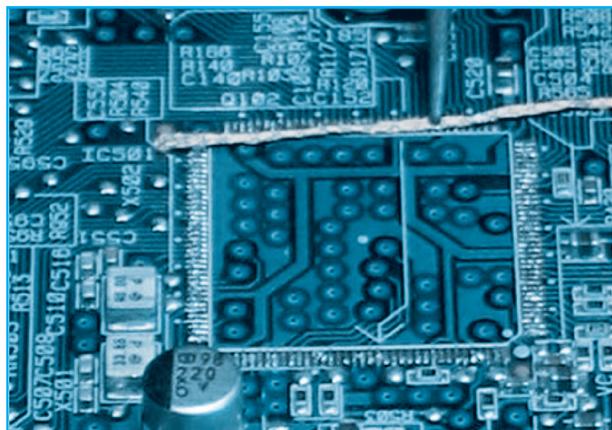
Para limpiar los Pads use flux y el soldador de gas.
